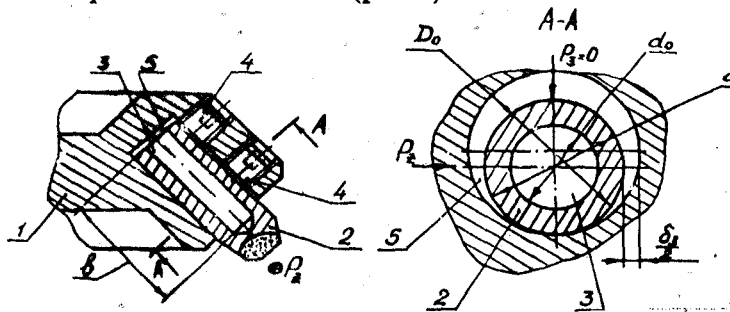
Торцевая фреза с цилиндрической режущей вставкой
